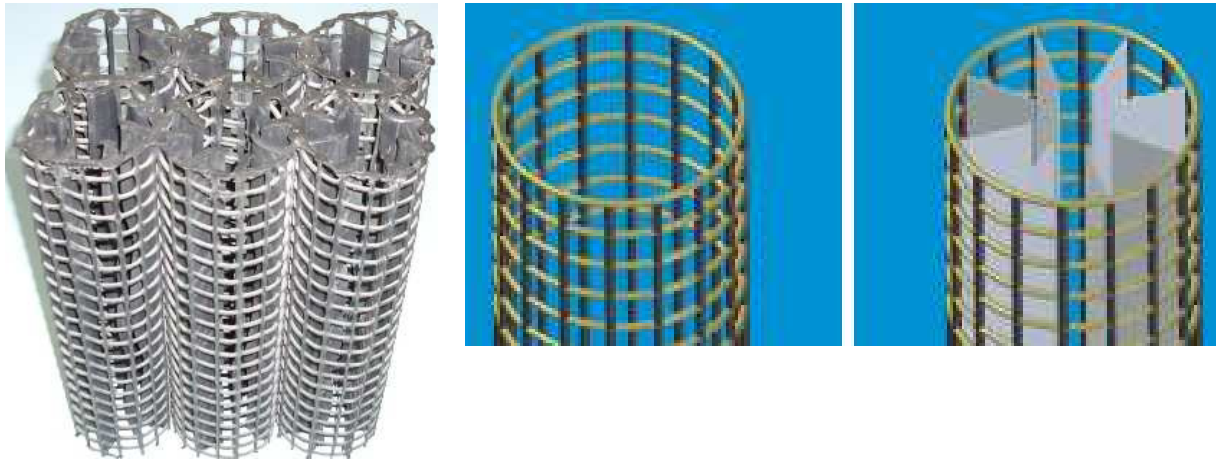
a) links: PE Röhren+Lamellen zu Block verschweißt; b) rechts: schematisch mit vertikalen Längsstreben und kreisrund horizontalen Streben
